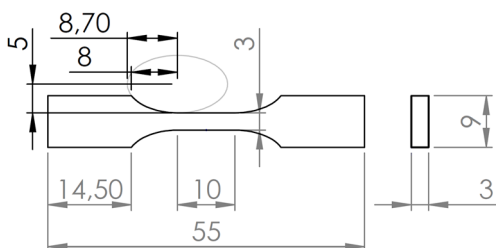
Geometria com dimensões em mm do corpo de prova #2.
